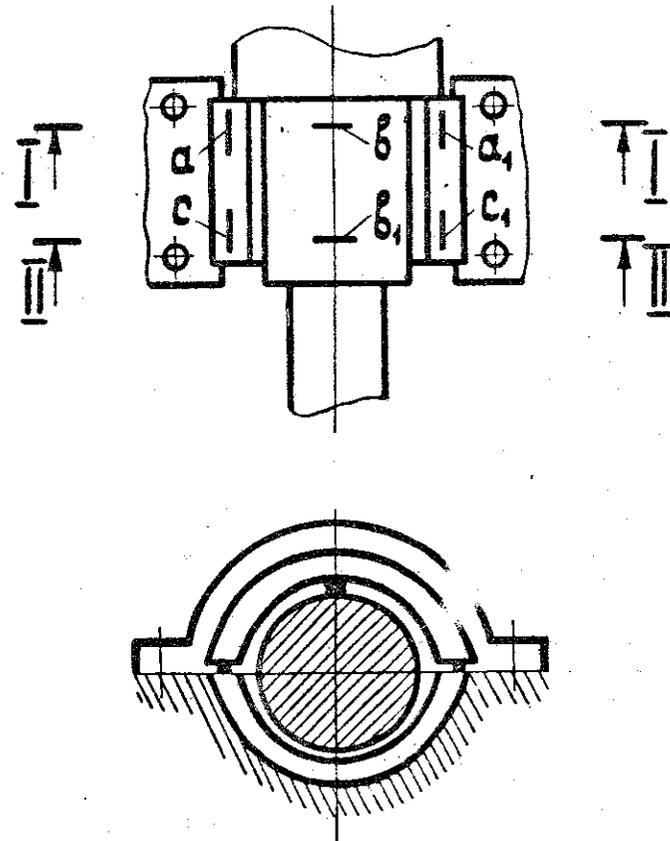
Расположение свинцовых проволок при проверке верхнего зазора во вкладыше
